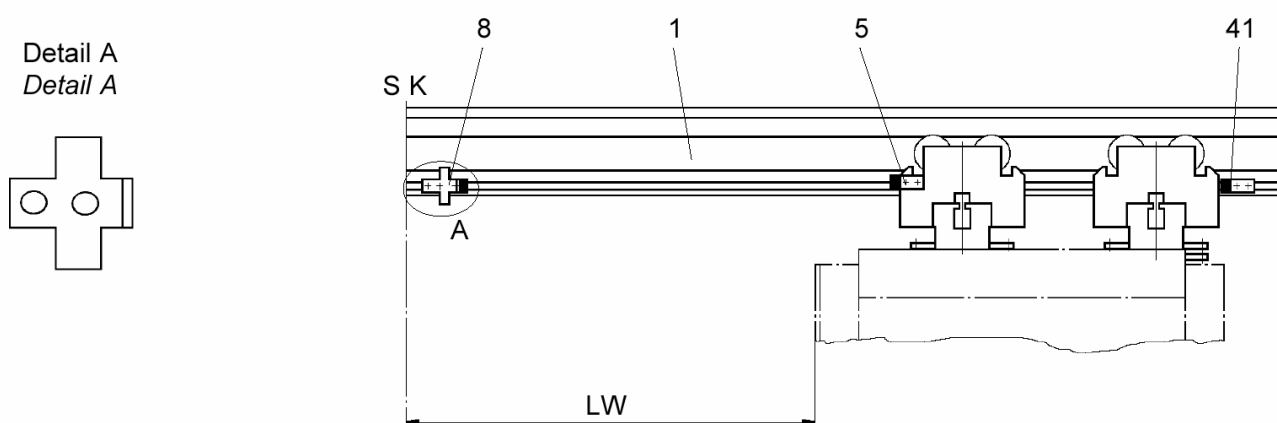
Стопоры ANSLA-S 1-створчатой раздвижной двери
